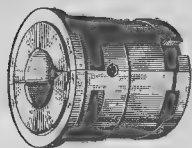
Вкладыш опорного подшипника жесткого типа
